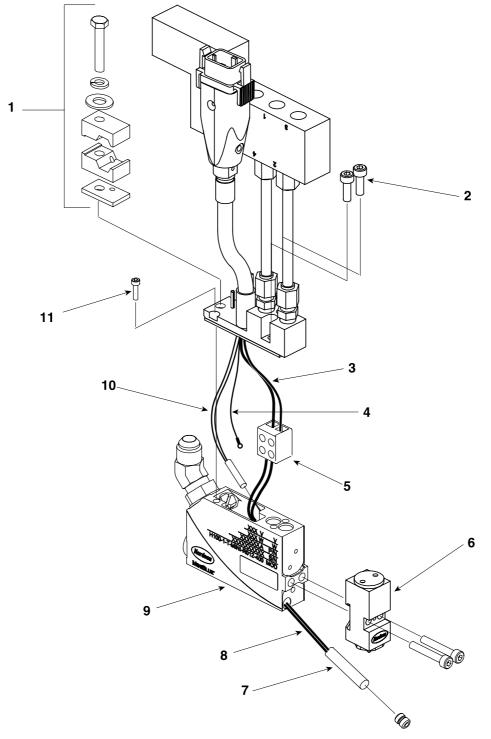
Remplacement d'une résistance chauffante ou d'une sonde RTD sur un pistolet mono-module extra-plat
